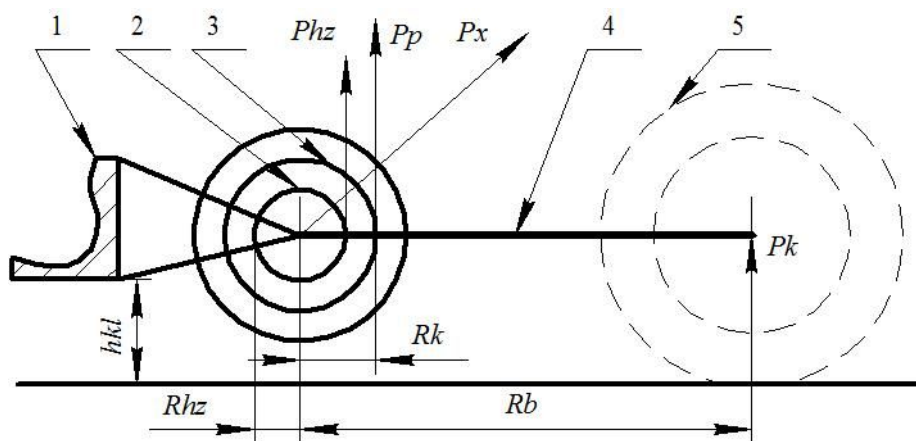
Розрахункова схема підвіски з гідропневматичною ресорою:
